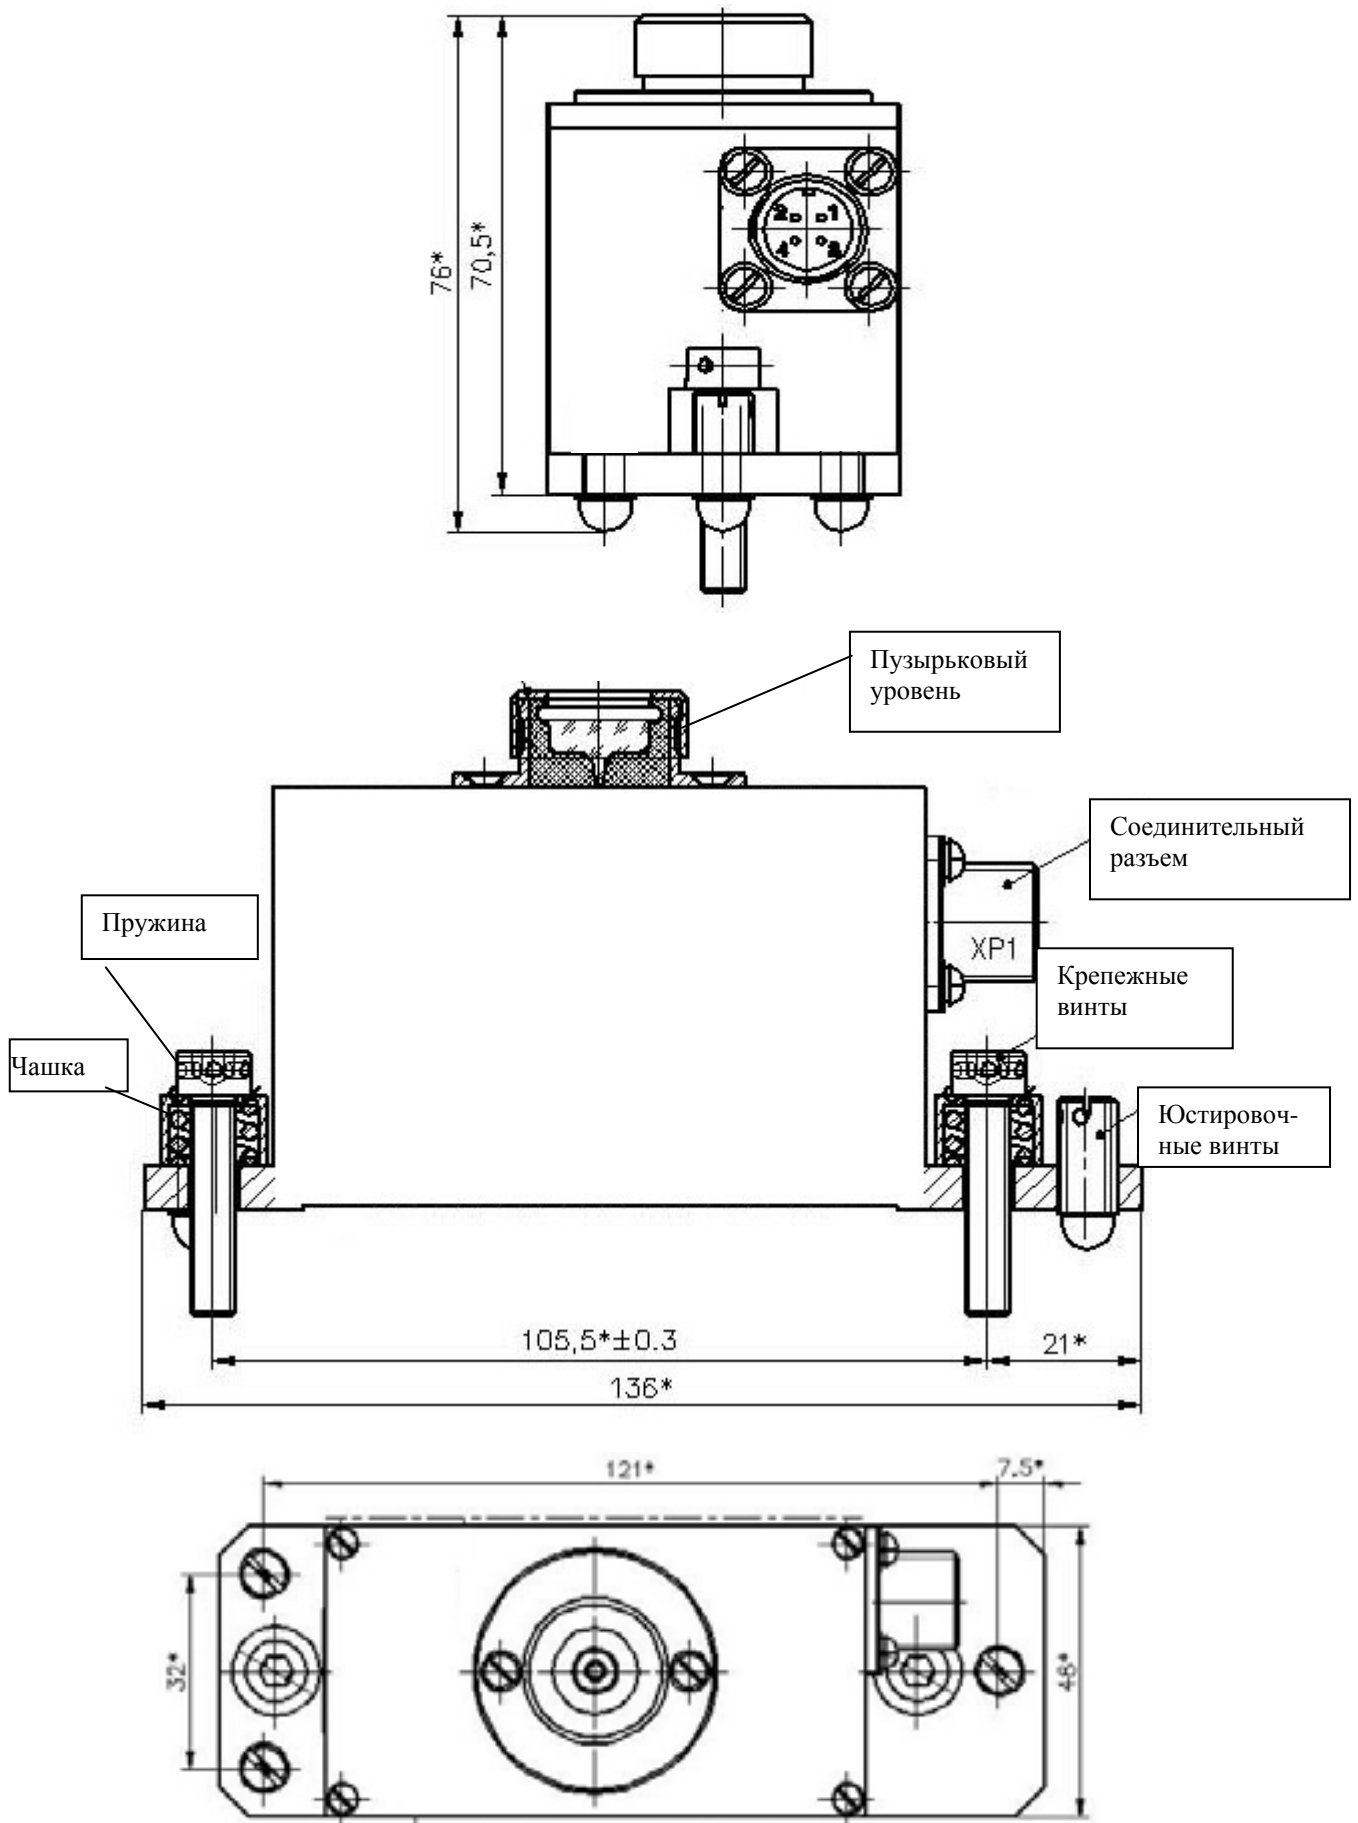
в Габаритные и присоединительные размеры датчика ВК-610.
